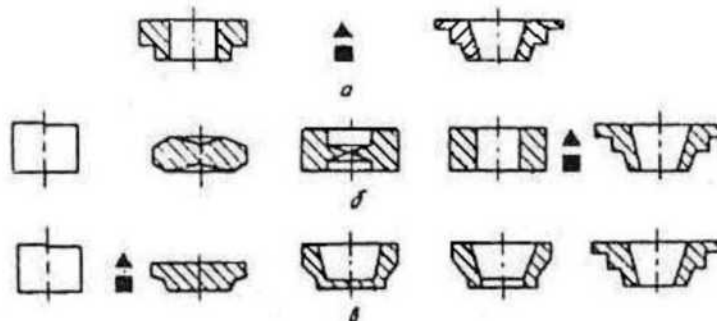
Примеры технологических вариантов штамповки тарелки пружин клапана: ▲ - отжиг; ■ - фосфатирование; а - из точной заготовки; б - из высаженной кольцевой заготовки с промежуточным отжигом; в - на многопозиционном автомате.
